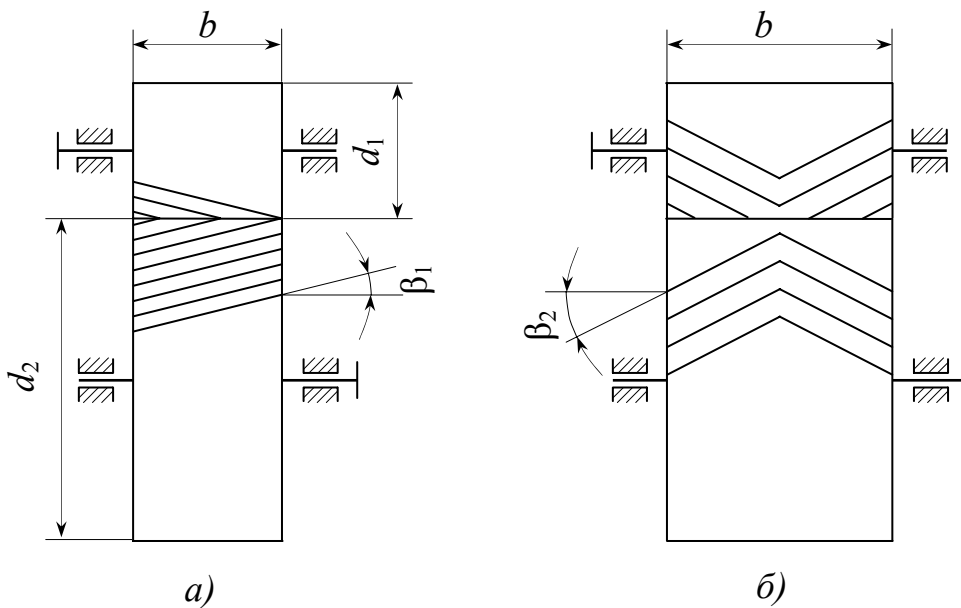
Кінематичні схеми циліндричних передач з непрямыми зубцями
